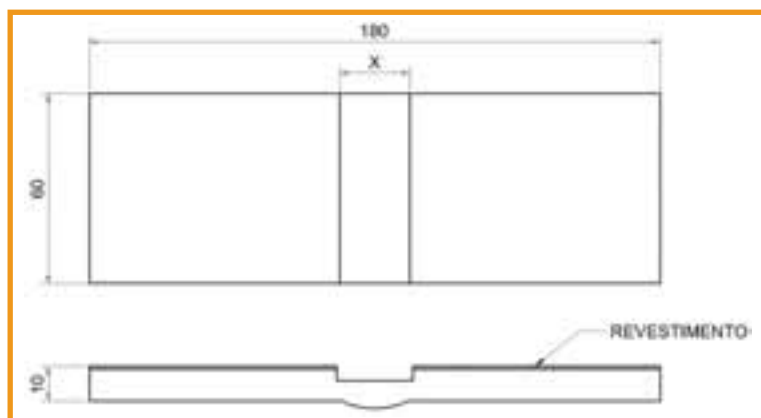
Ilustração de corpo de prova usinado para remoção da parte rugosa da região de solda
